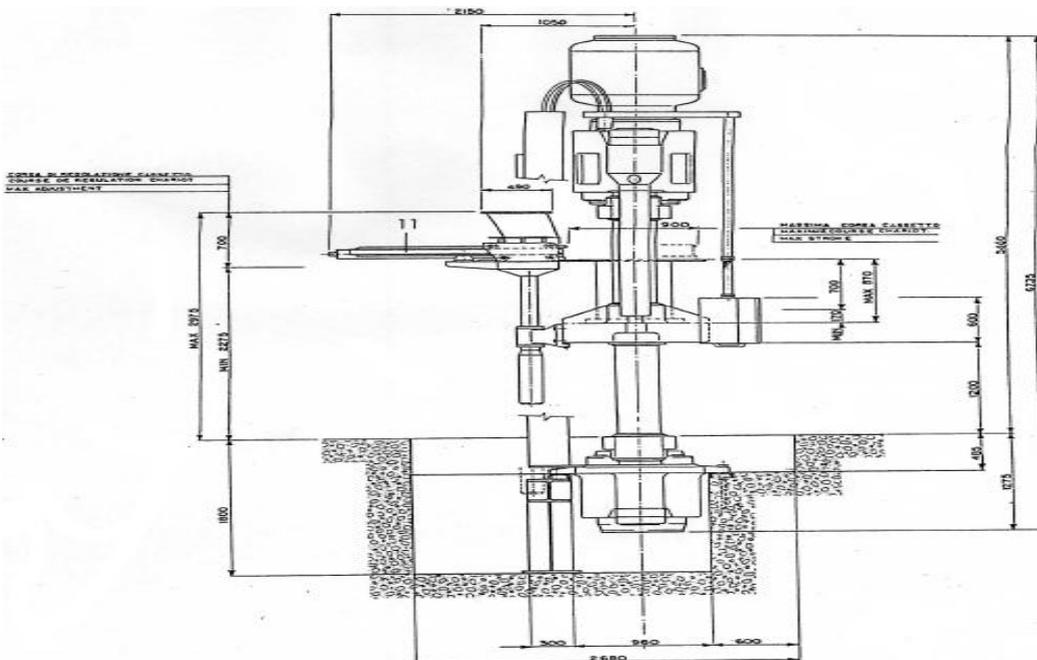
Vue de gauche de la presse MATRIX HS 550L [3].
